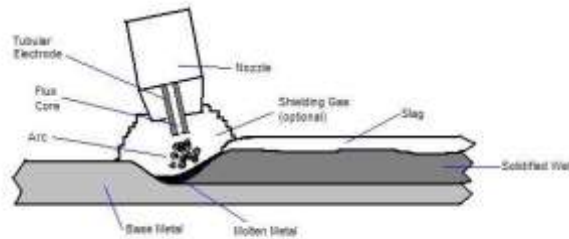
FCAW: FLUX CORE ARC WELDING
